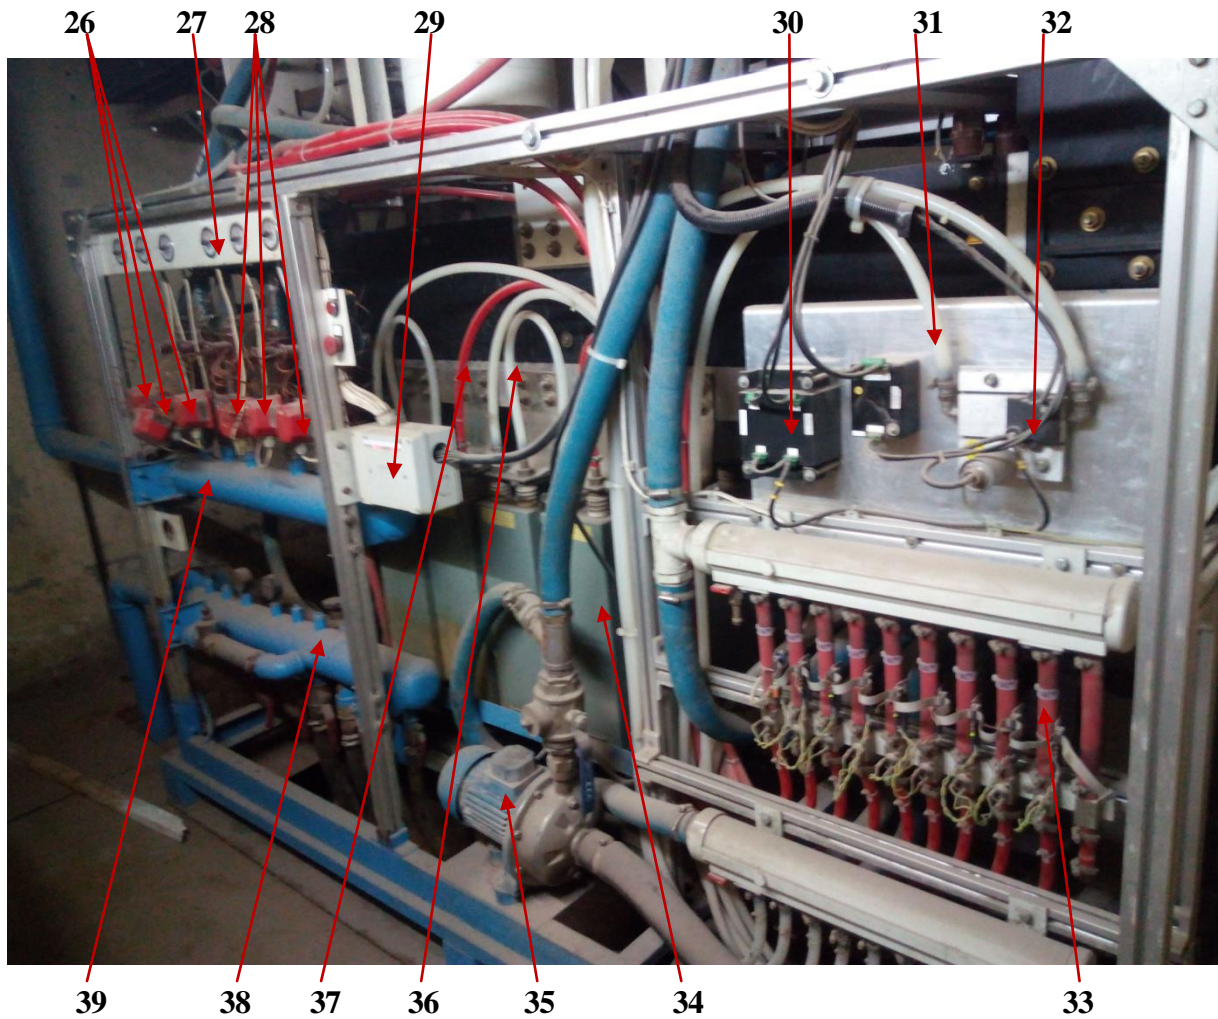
Vue de L'arrière de la plate forme en béton sous le four.
